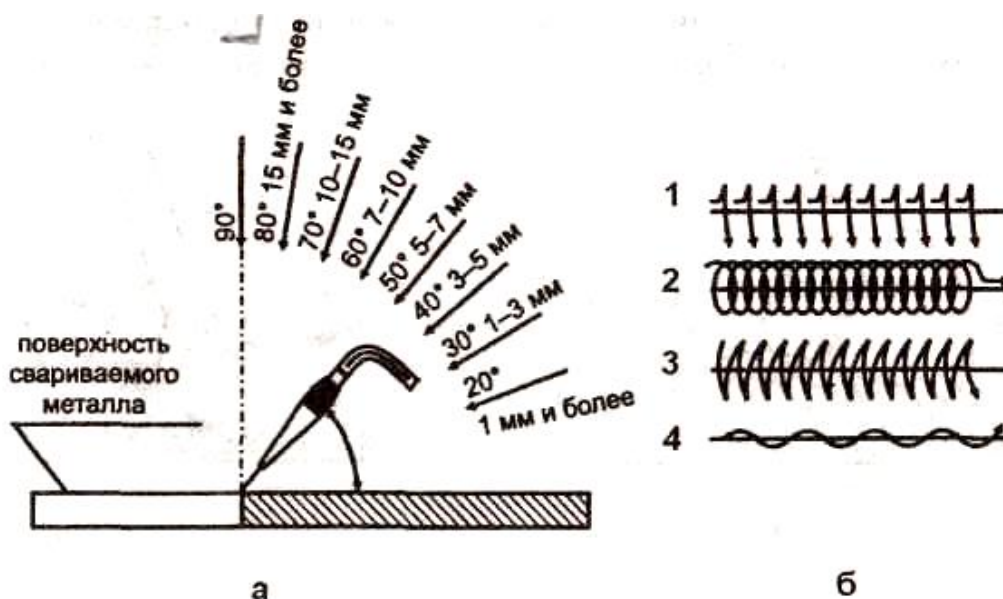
Углы наклона мундштука горелки при сварке различных толщин (а) и способы перемещения мундштука горелки (б):
